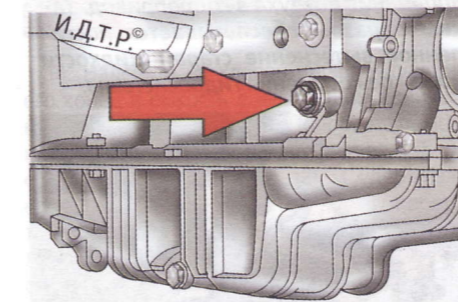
Заглушка отверстия для установки фиксирующего стержня коленчатого вала
